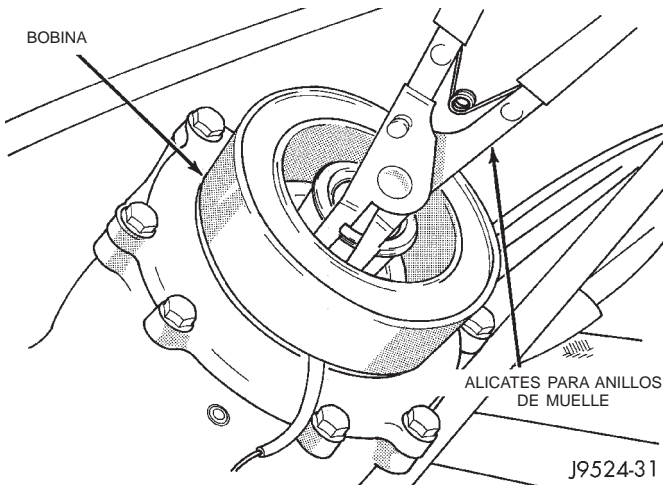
Desmontaje del anillo de muelle de la bobina de campo del embrague
